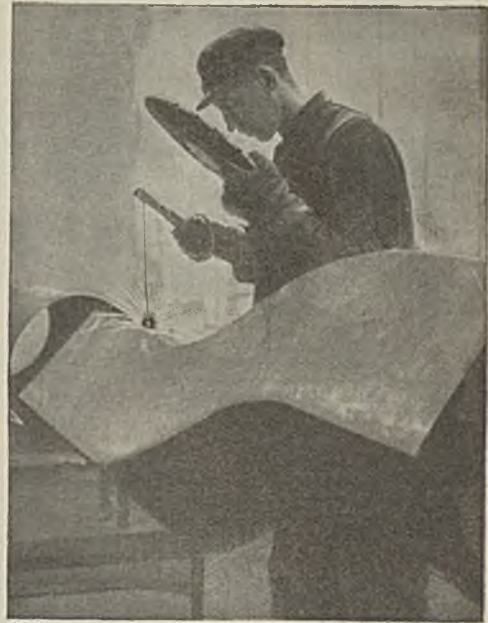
Schweißen von Ventilatorröhren.
